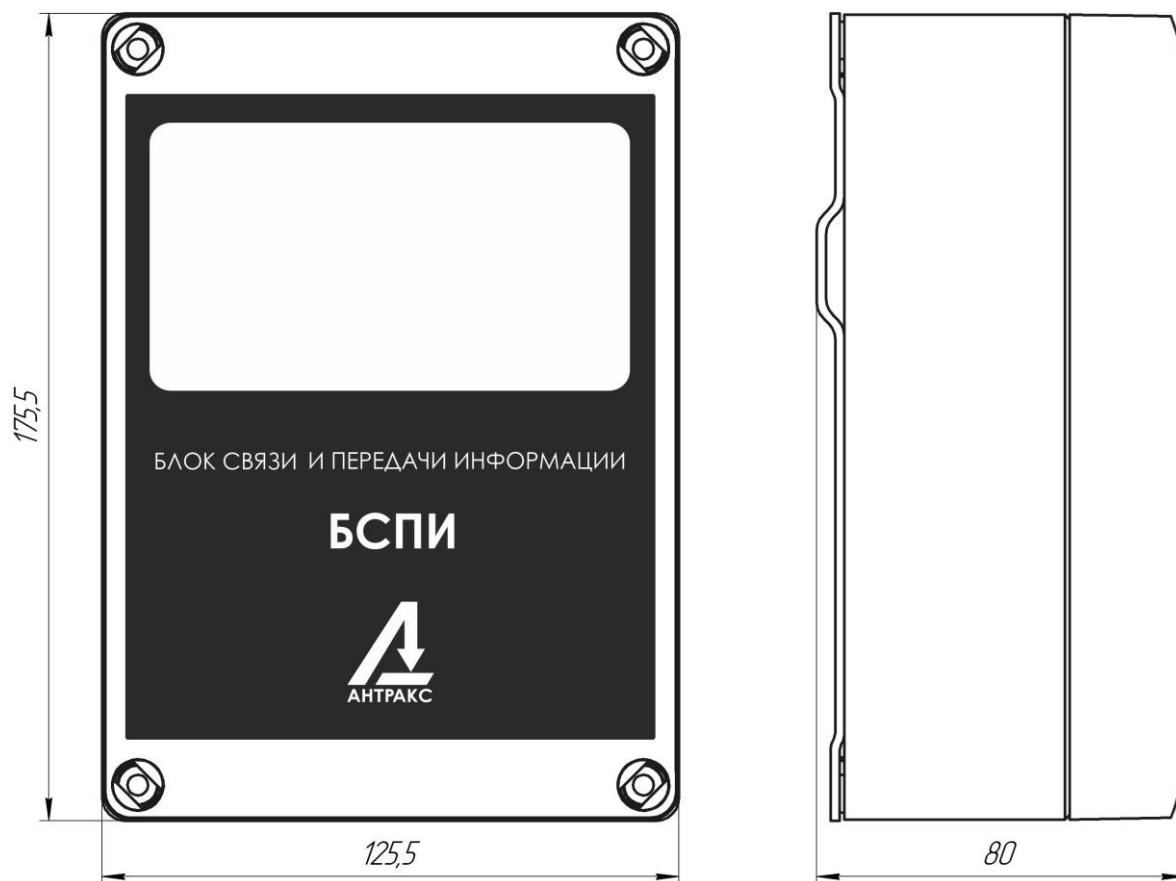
Габаритные размеры блока БСПИ-ЗЛ-МР
